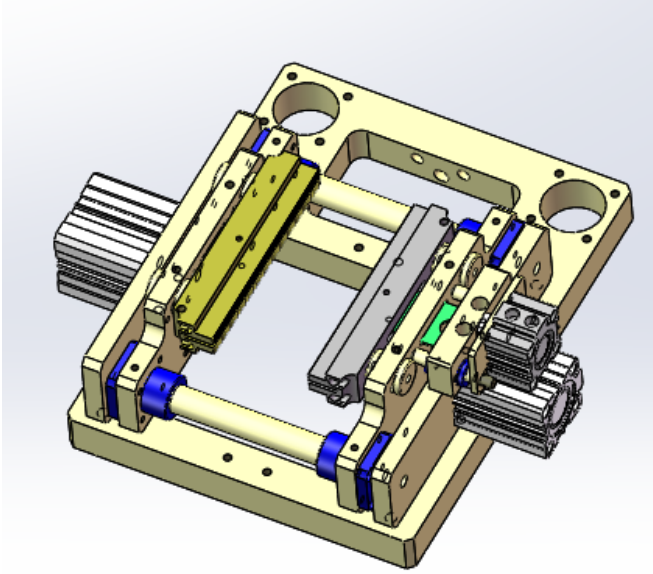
横封机构示意图 FIG. 33 schematic diagram of horizontal sealing
